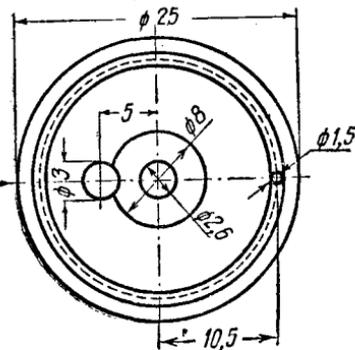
б. Дет. 339. Крышка регулирующего колпака
